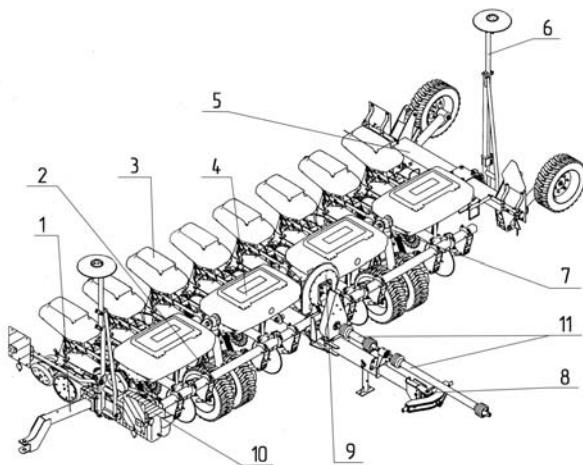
Конструкційна схема сівалки «Вега-8»
